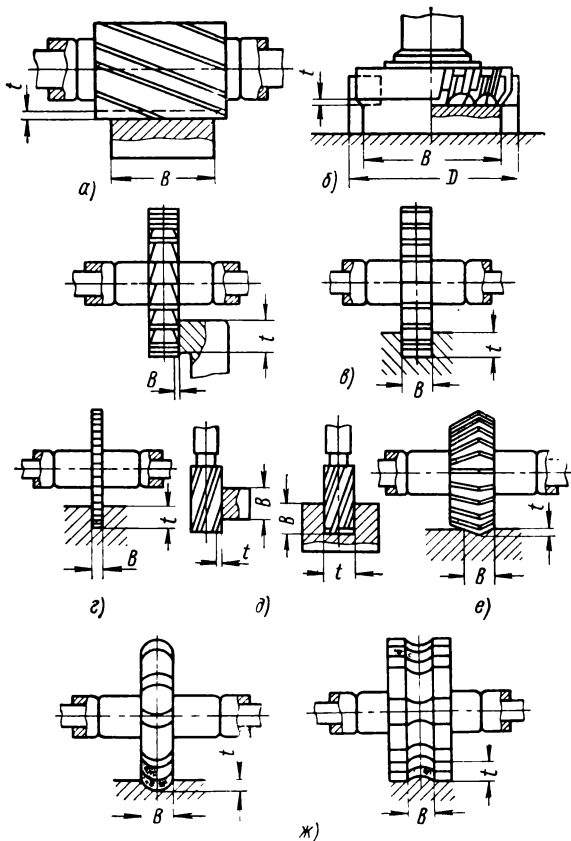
Ширина и глубина при фрезеровании фрезами: а — цилиндрической; б — торцовой; в — дисковой; г — отрезной и прорезной; д — концевой; е — угловой; ж — фасонной радиусной
